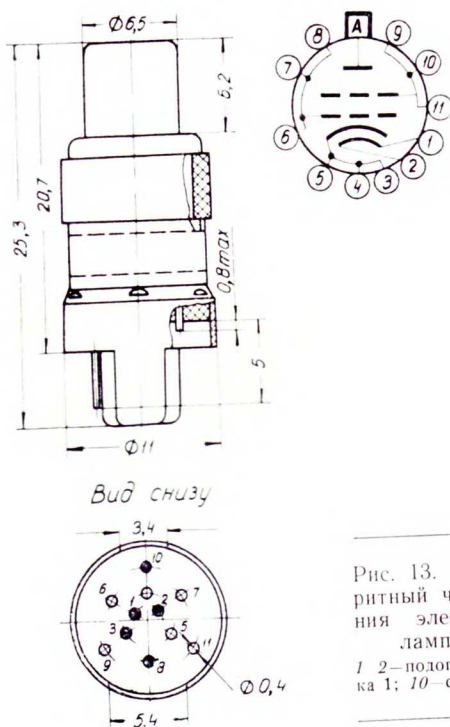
Внешний вид, габаритный чертеж, схема соединения электродов с выводами ламп 6Э13Н и 6Э14Н
